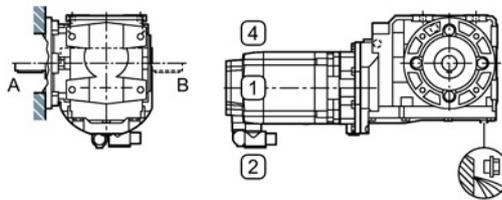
Einbaulagen für Kegelradgetriebe B, Fußausführung, Baugröße 39 - 49, 2-stufig
